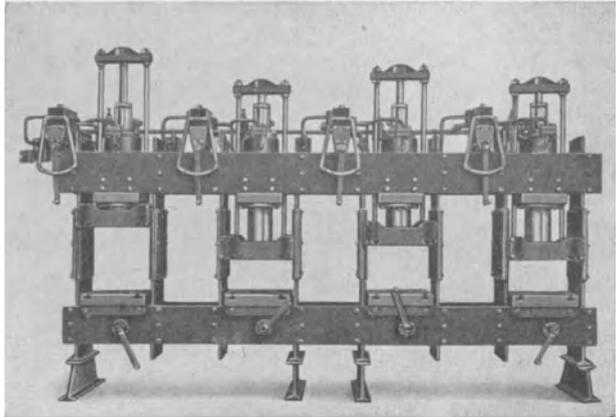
Reihenpresse mit 4 Druckkammern von je 60 t Druckvermögen und 3 Leerkammern zum Unterbringen von Preßmasse oder Wärmeschränken.
